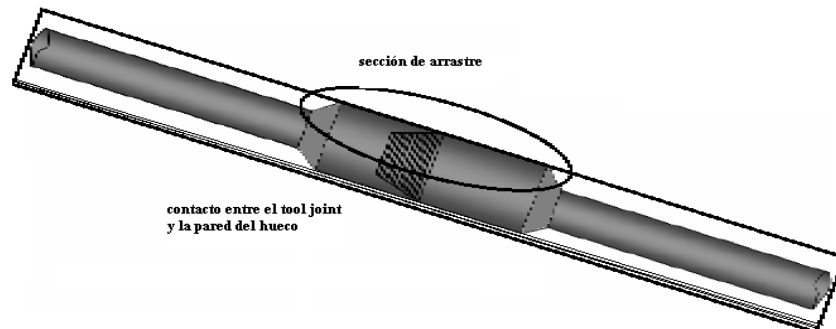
Esfuerzos y área de contacto en el Tool Joint de dos juntas de Drill Pipe, cortesía de Weatherford
